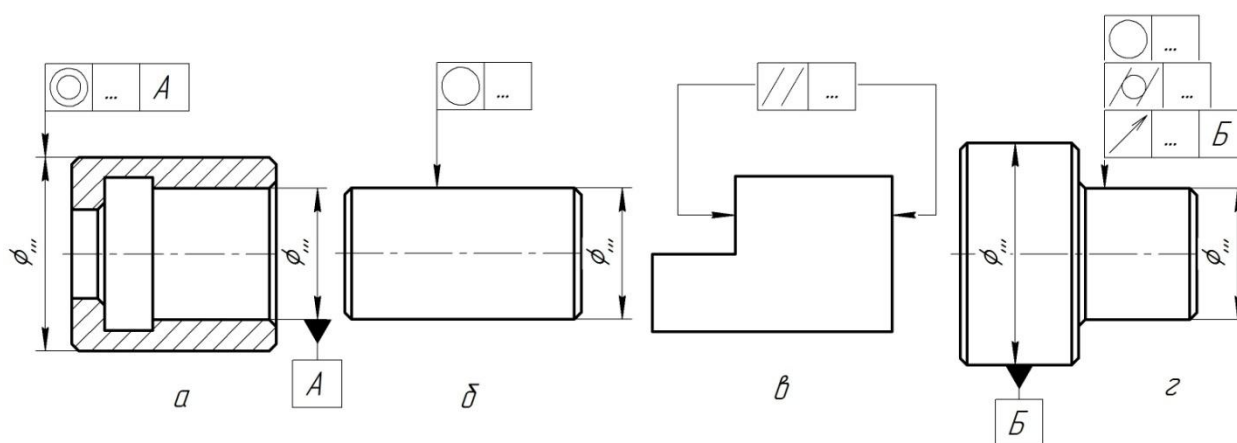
Нанесение допусков отклонения точности формы и взаимного расположения поверхностей детали
